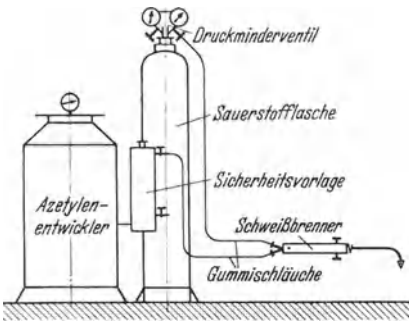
Grundform einer beweglichen Azetylen-schweißanlage.
